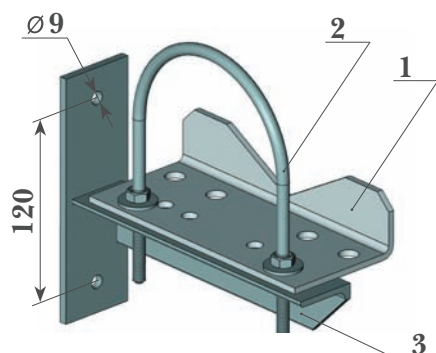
Общий вид крепления коллектора стенового ККС в сборе
